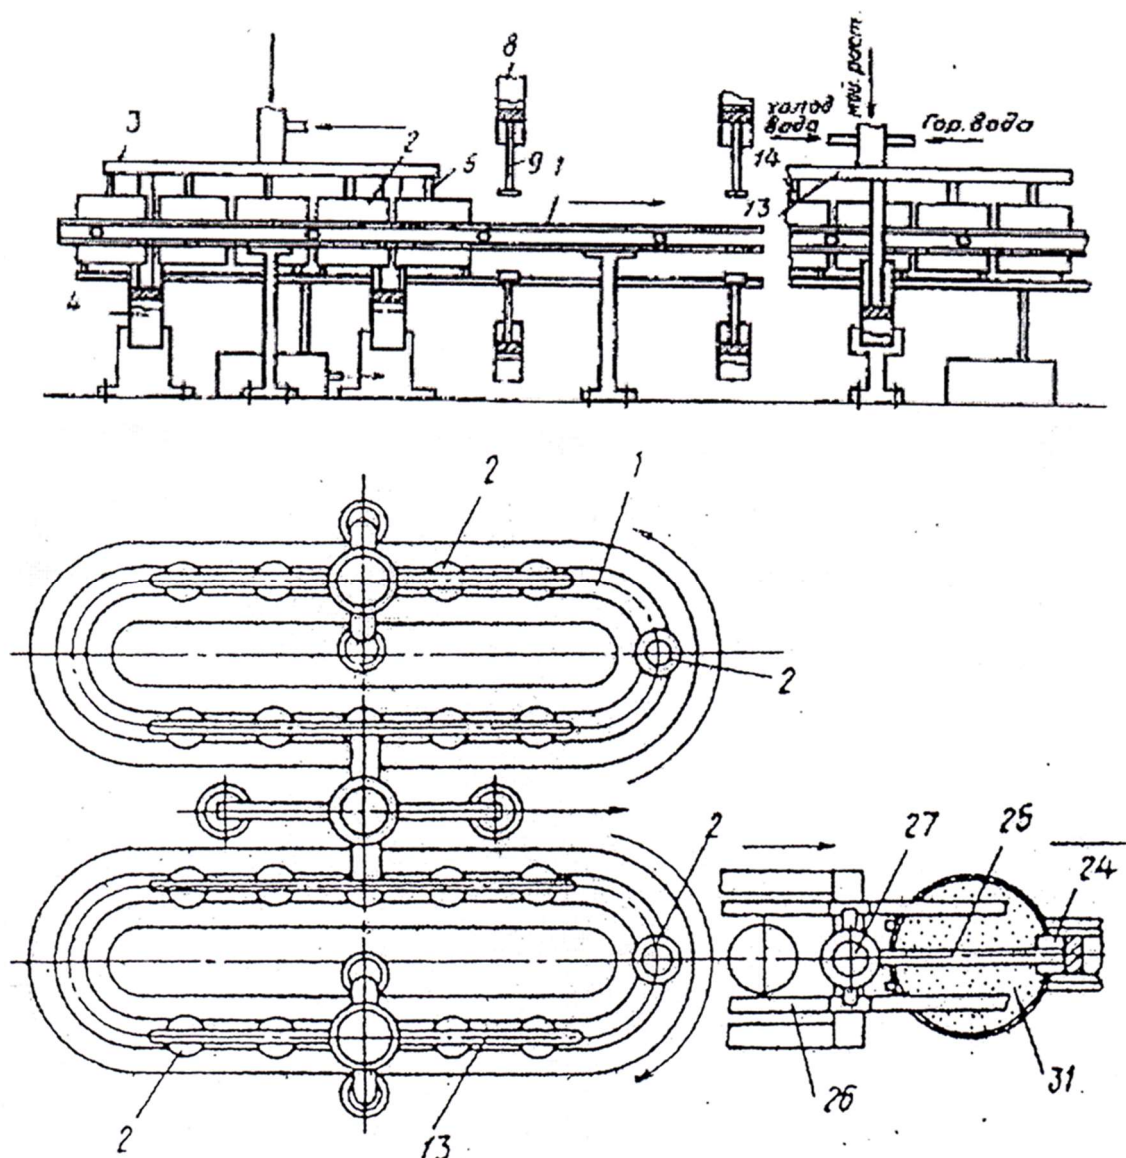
Показаны устройства для розлива сырного зерна в формы и прессования зерен в формах, а также, моечное устройство.
